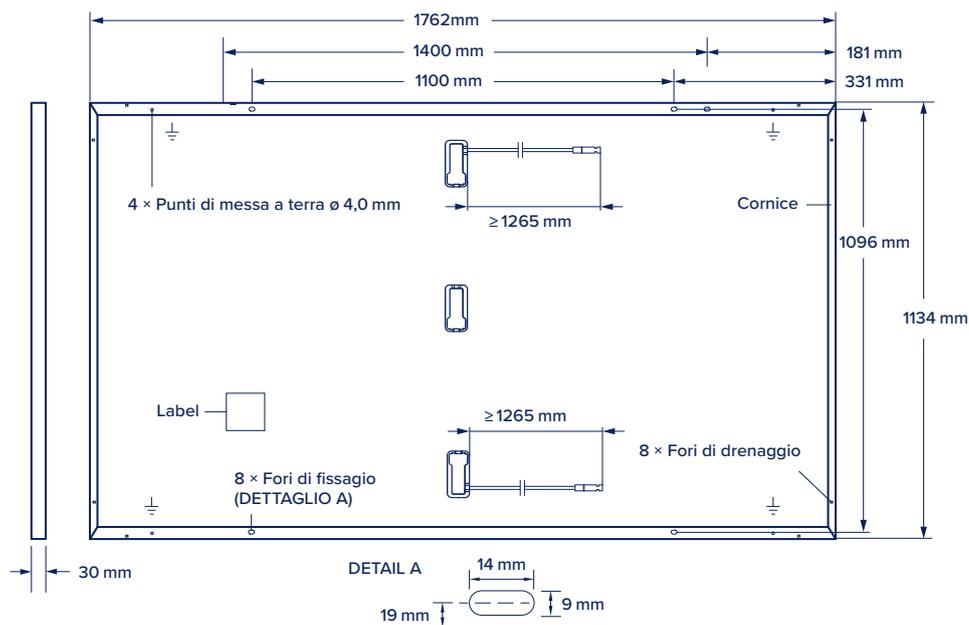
Dimensioni d'ingombro (in mm) e componenti per
